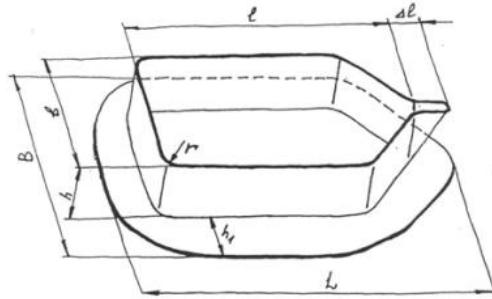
Взаимное расположение контейнера и плоской листовой заготовки.
